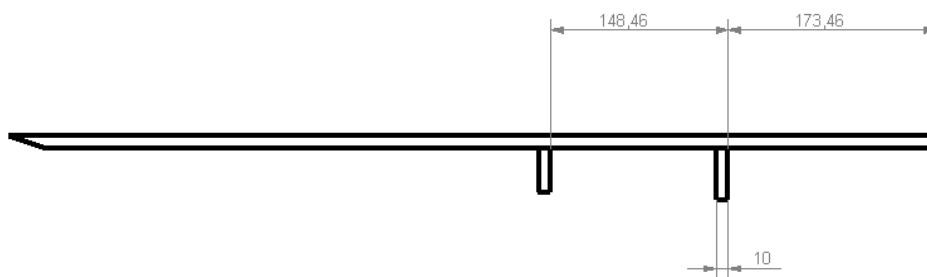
Posicionamiento de los refuerzos transversales.
